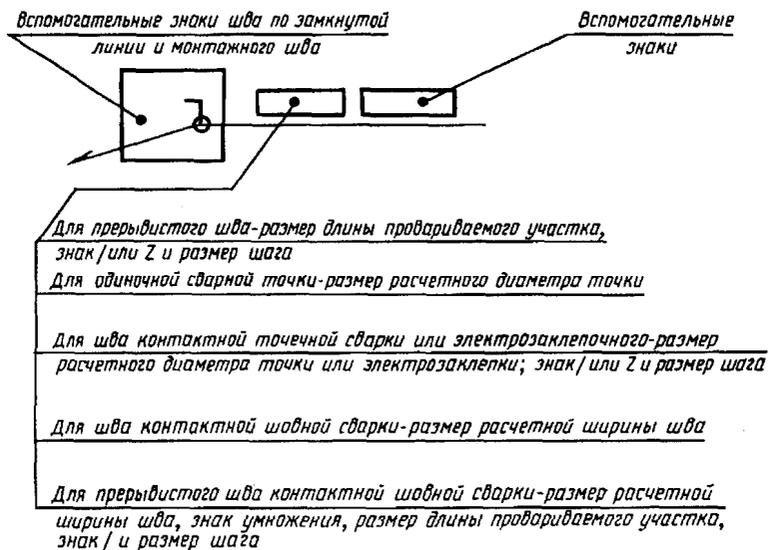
Структура условного обозначения нестандартного сварного шва
